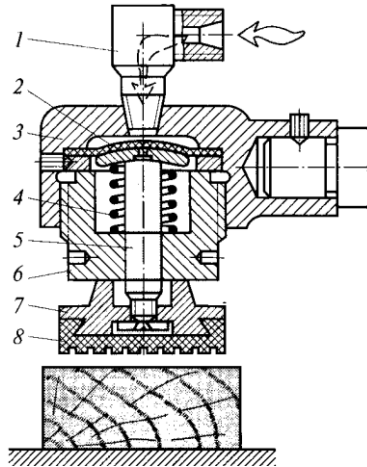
Гідрозатискач: 1 – штуцер; 2 – мембрана; 3 – корпус; 4 – пружина; 5 – шток; 6 – склянка; 7 – черевик; 8 – накладка
